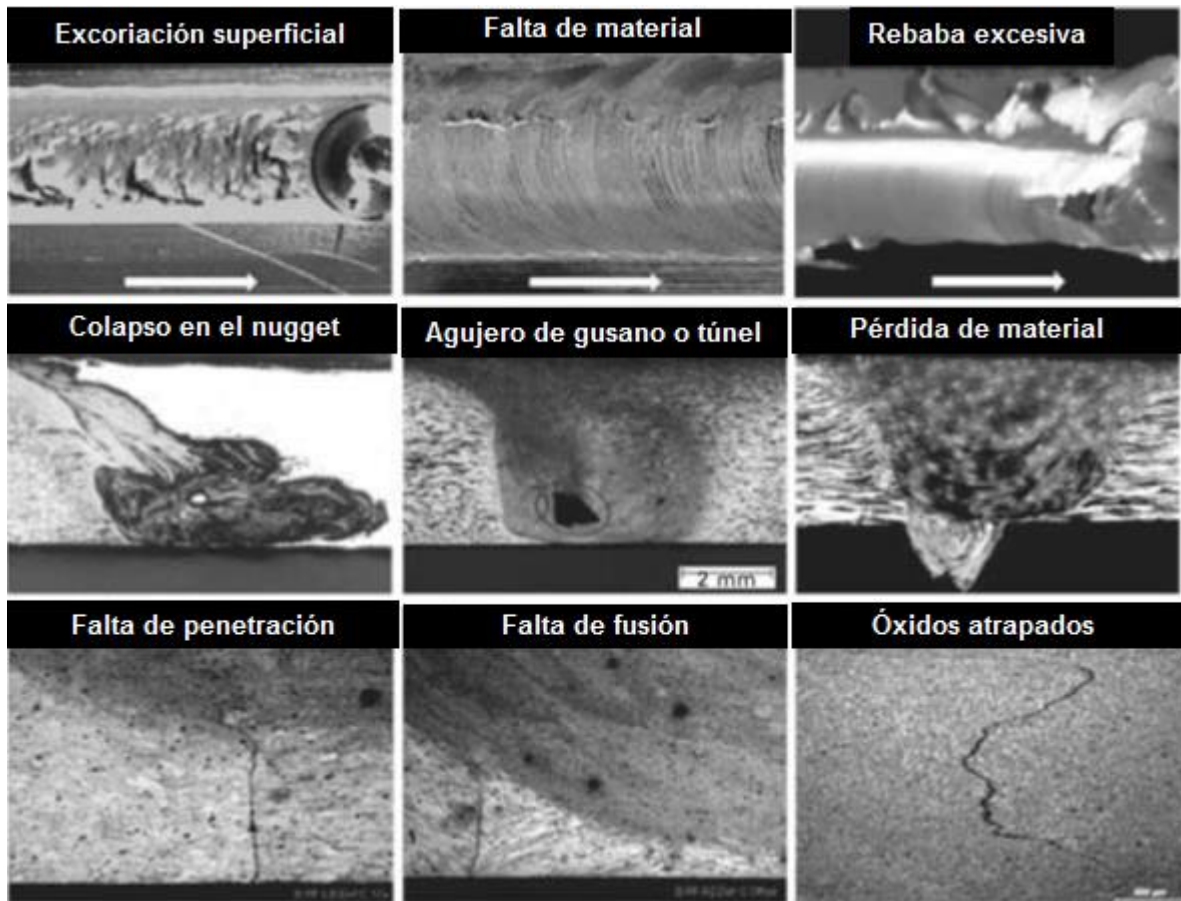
Algunos defectos que se presentan en la soldadura por fricción-agitación (FSW) (33).
